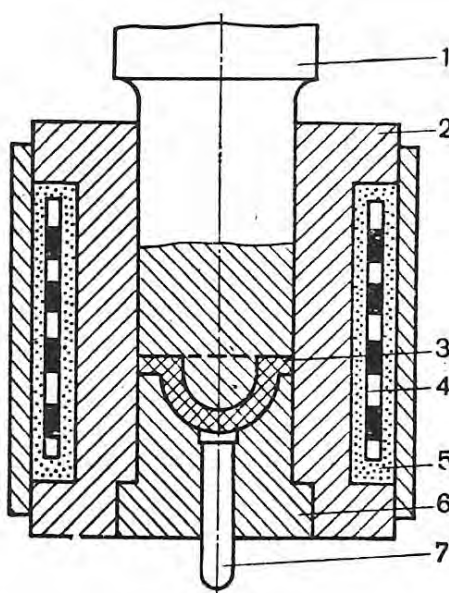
Пресс-форма для компрессионного прессования: 1 - пуансон; 2 – обойма; 3 - деталь; 4 – нагревательный элемент; 5 - рабочий изоляция; 6 – матрица; 7- выталкиватель.
